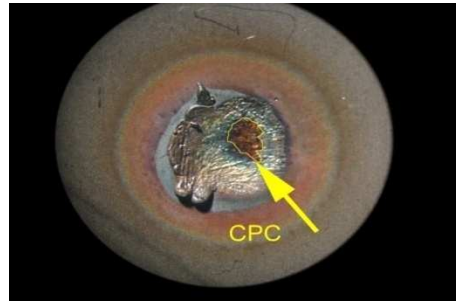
4. Punto de soldadura en la Probeta de 1 mm a 5x.
